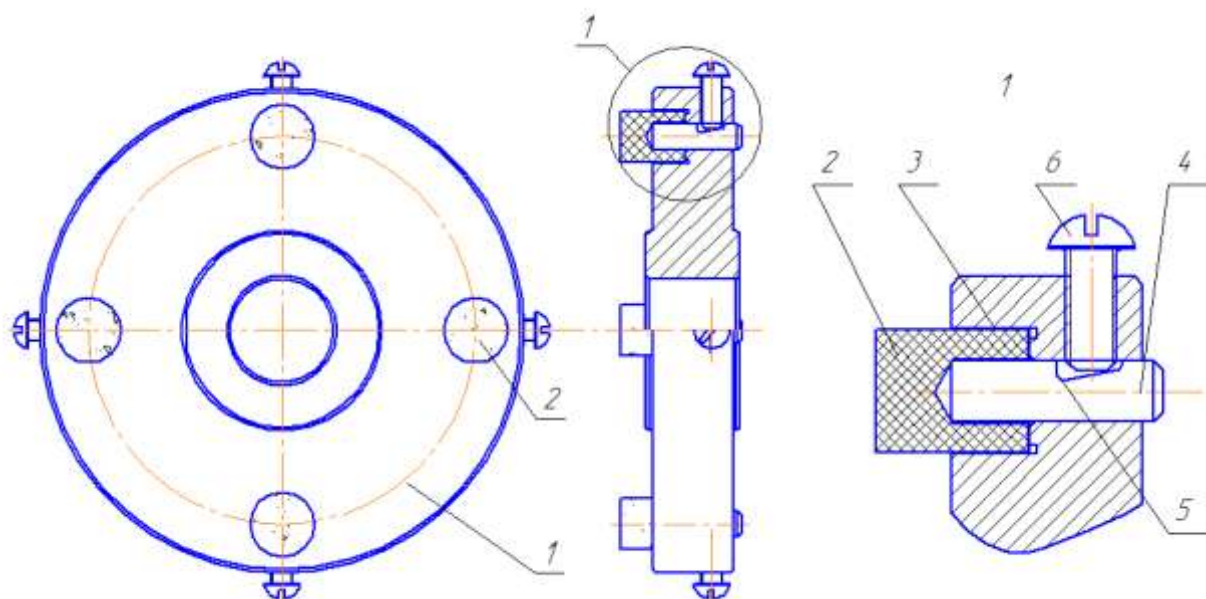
Конструкция специального шлифовального круга: 1 - корпус; 2 - алмазно-абразивные шлифовальные сегменты; 3 - клеевая прослойка; 4 – штифт с замковым пазом; 5 - конусный паз; 6 - фиксирующий винт
